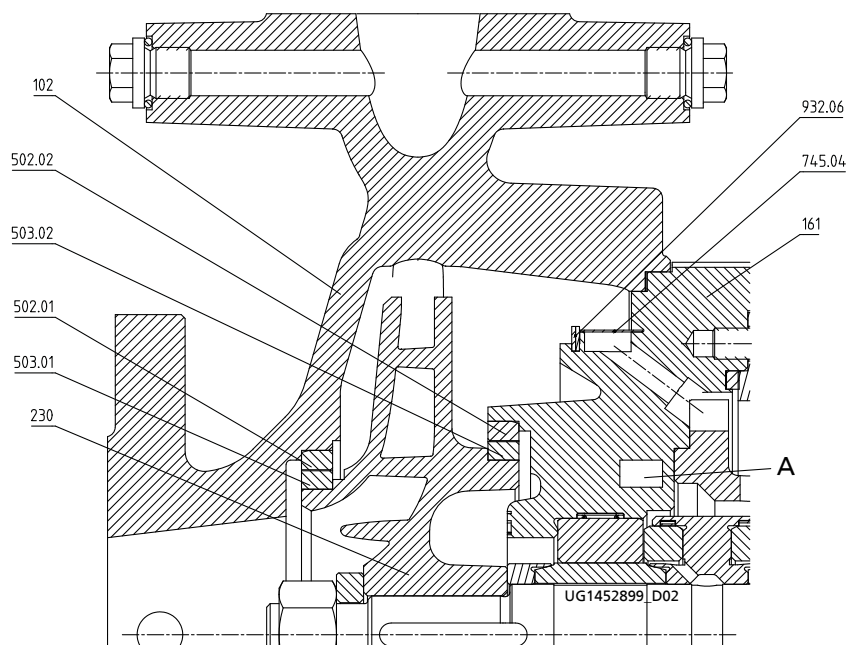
Ausführung Spiralgehäuse mit Ringfilter, Heizkammer, Spaltring und Lauftring
